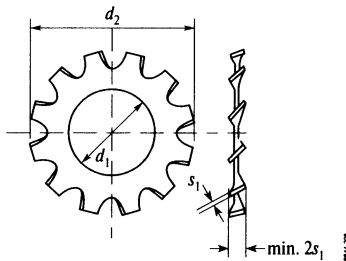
Тип А — с внешними зубьями: стопорные шайбы
